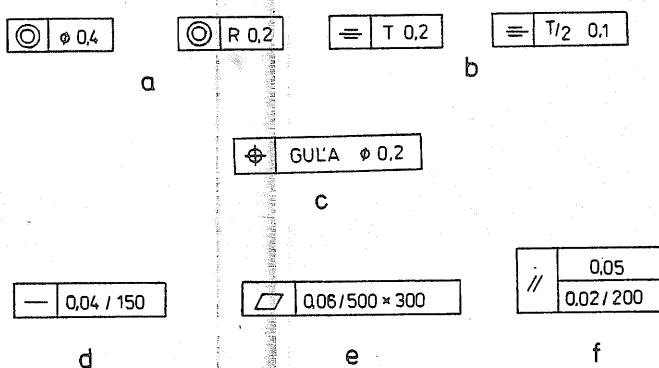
Tvary značiek na predpisovanie tolerancií tvaru a polohy
